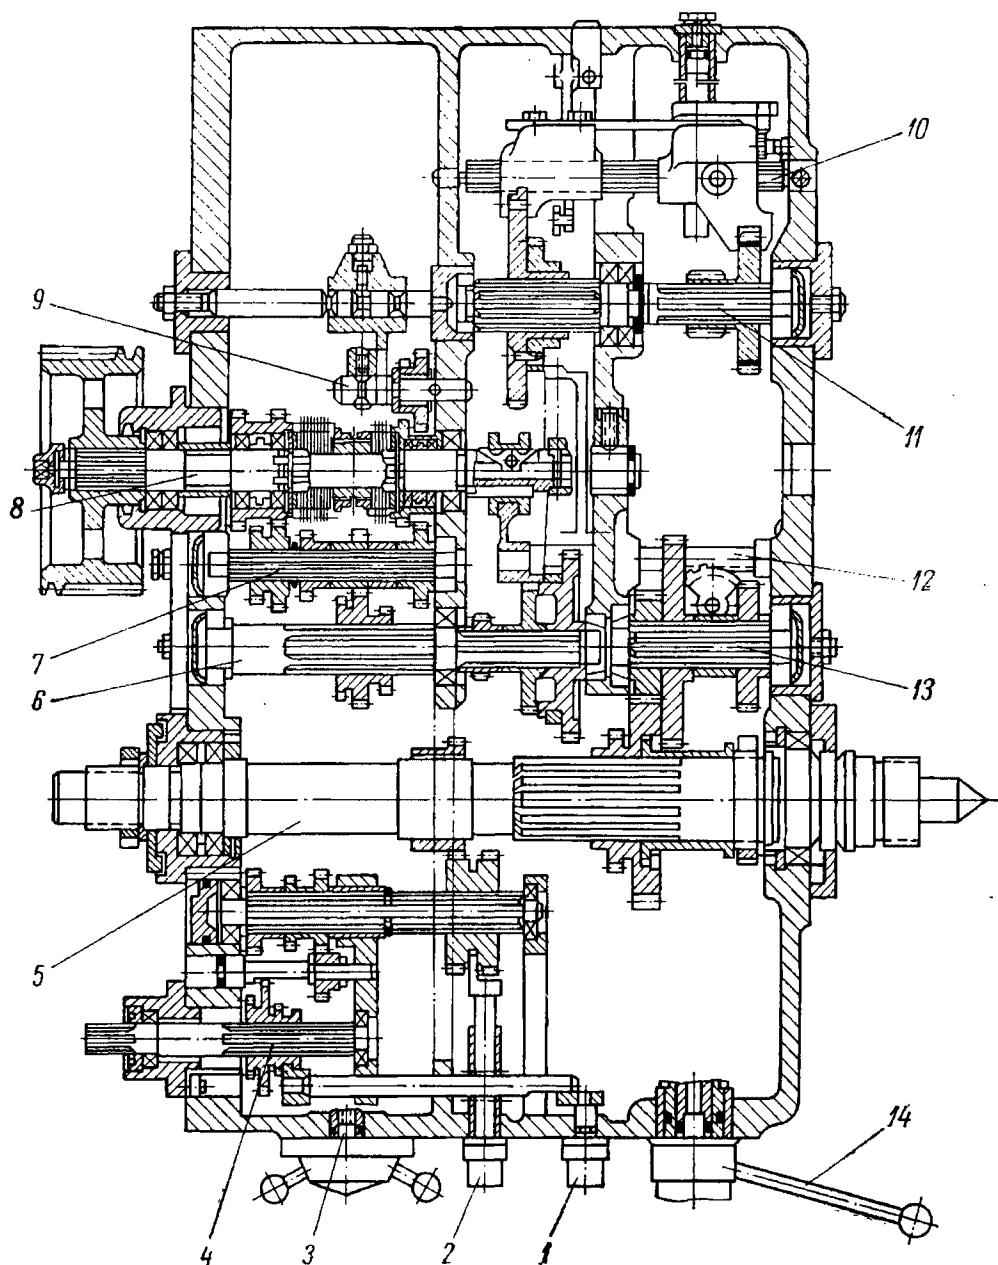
Развертка передней балки токарно-винторезного станка моделей 1К62
